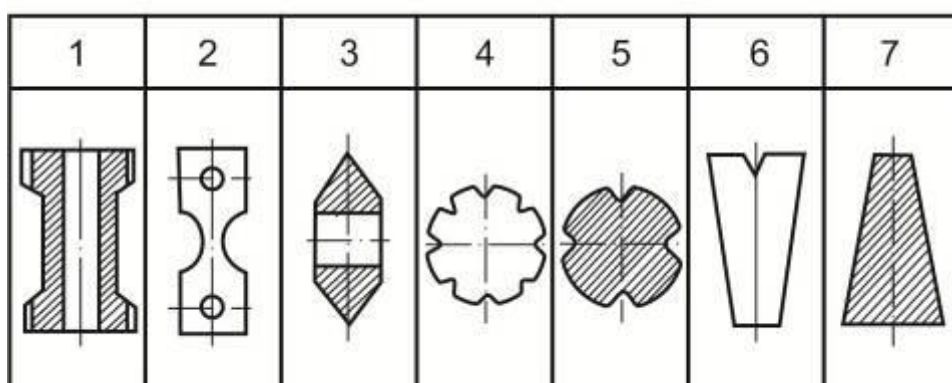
Типы образцов для испытаний на термоусталость: 1 – образец Коффина (трубчатый); 2 – плоский корсетный; 3 – дисковый; 4 – диск с концентраторами; 5 – цилиндр с канавками; 6 – плоский с концентратором; 7 – клиновидный.
